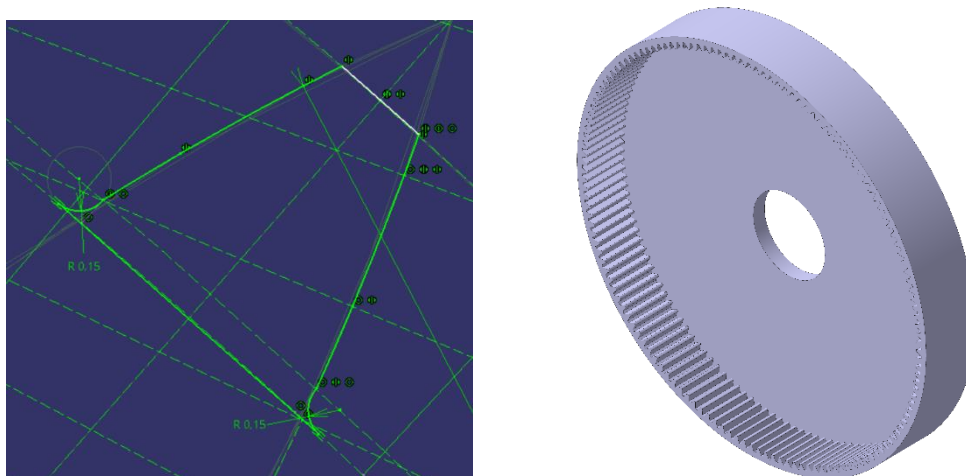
a la izquierda: 'sketch' del diente del engranaje 4. A la derecha: el modelado final del engranaje 4.
